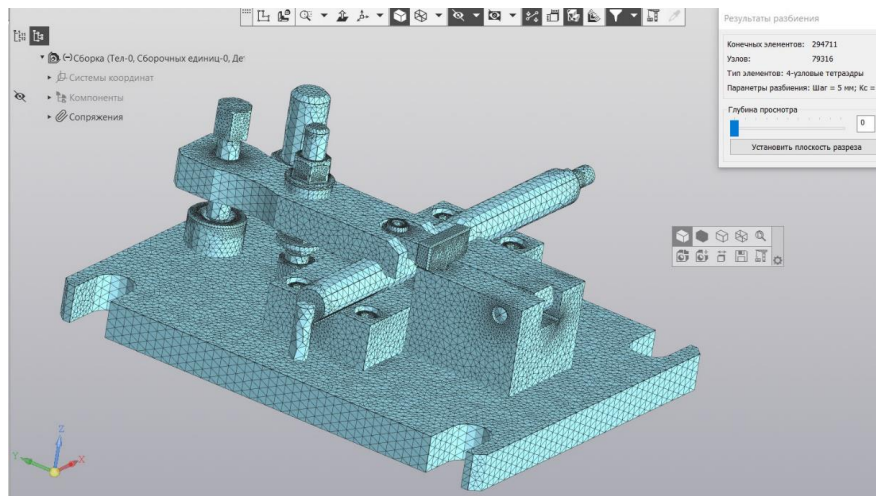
Конечно-элементная сетка приспособления с приложенными нагрузками и закреплениями
